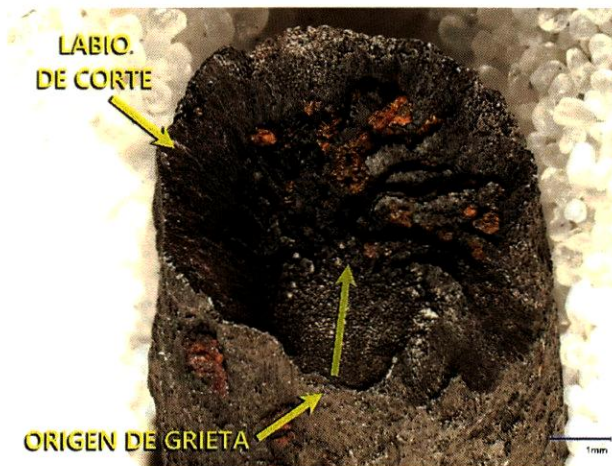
Cara del alambre fracturado No. 1 de F-A-BM-12.
